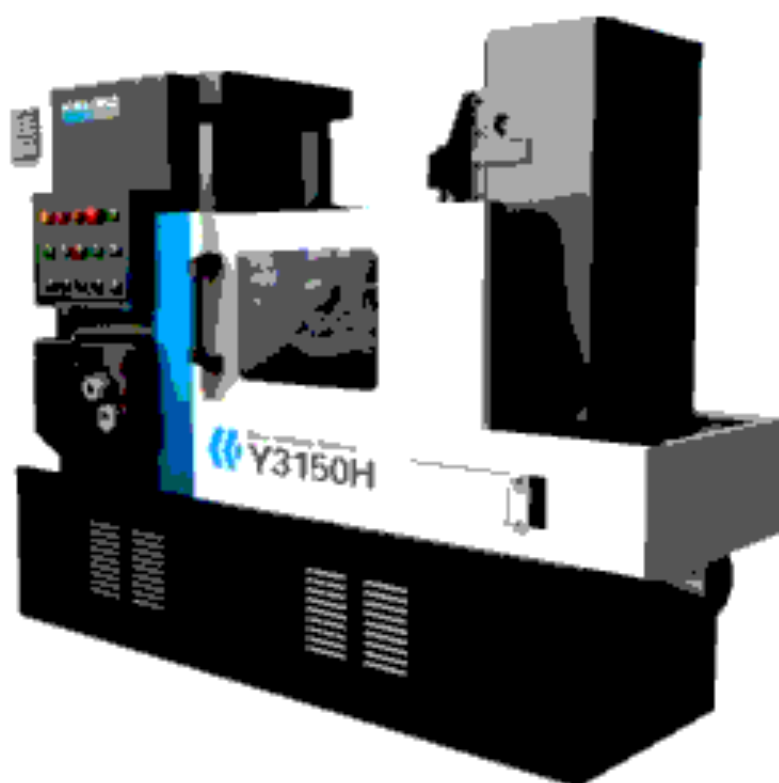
Зубофрезерный станок с ЧПУ модели Y3150H
